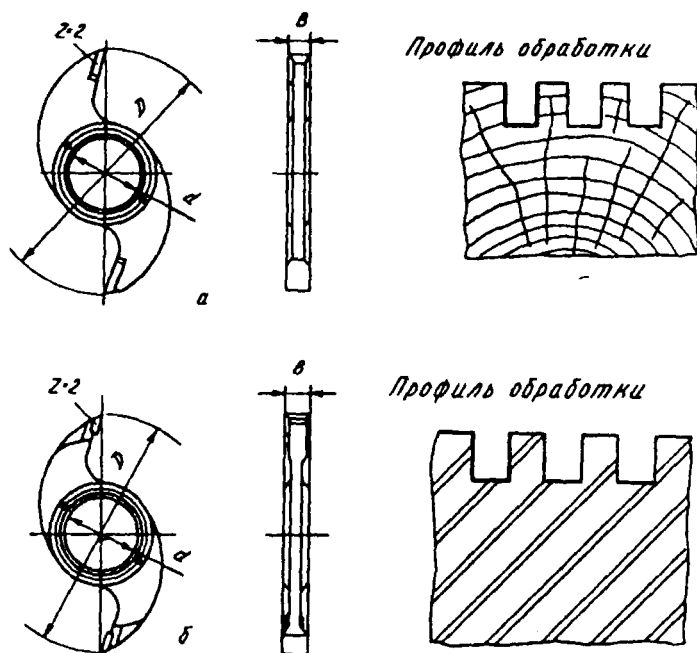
Фрезы для обработки прямых ящичных шипов:
